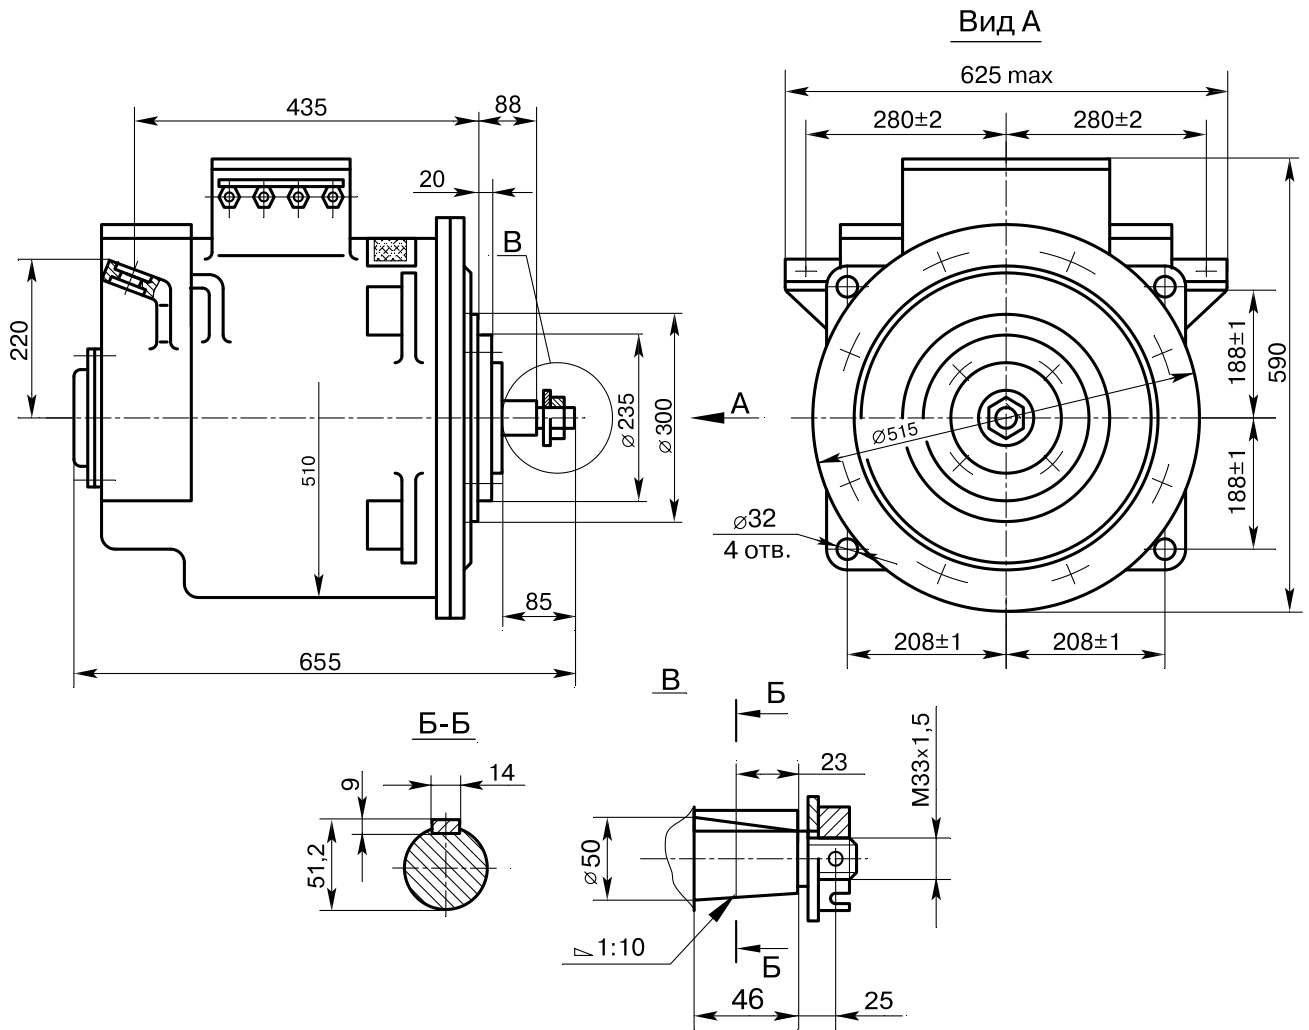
Габаритные и установочные размеры электродвигателя ДРТ-33
